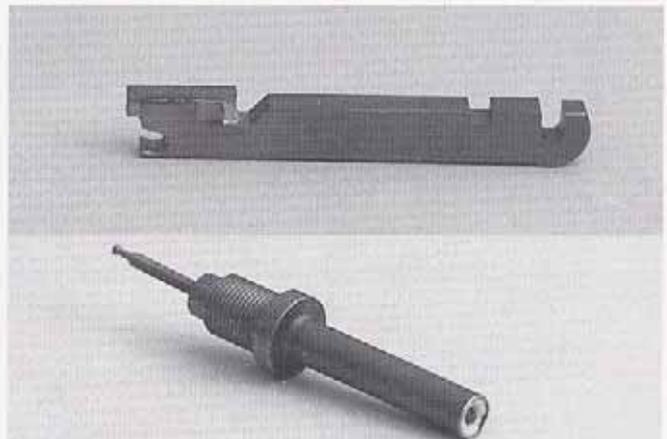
oben: Drehmeißel mit eingelöteter Hartmetall-Schneide. Bild 16 unten: Heizelement mit verlöteter Verschraubung
